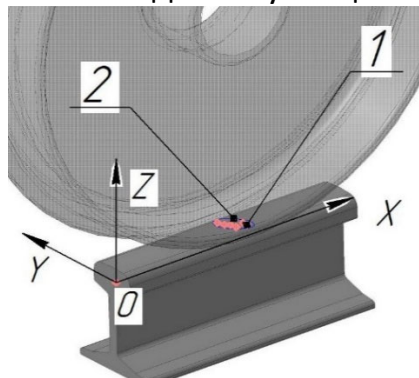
Опорна поверхня фрикційної пари колесо-рейка
